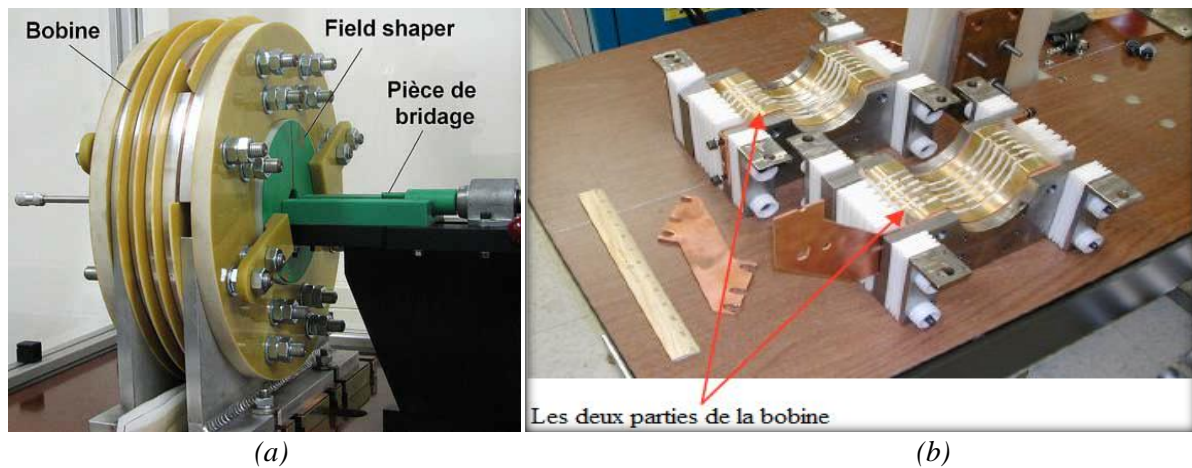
(a) Bobine multi spires de la machine de soudage, (b) la bobine multi spires démonté [13]
